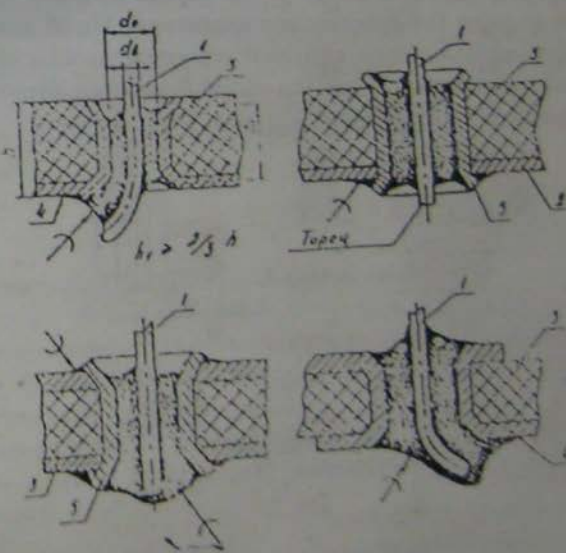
Рекомендуемые формы паяных соединений на печатных платах с металлизированными отверстиями: 1 - вывод электрорадиоэлемента; 2 - печатный проводник; 3 - подложка печатной платы; 4 - колпачковая пайка; 5 - пайка для заделки.
